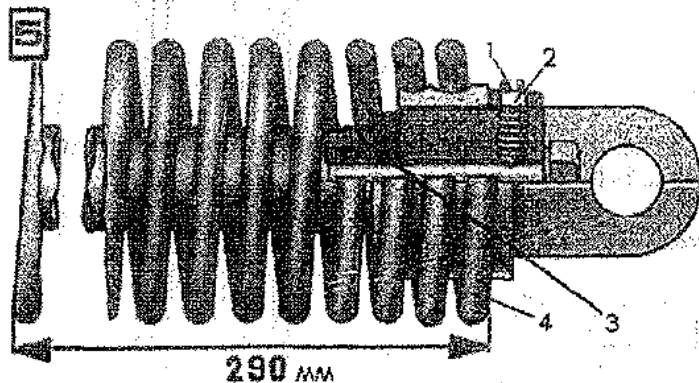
Схема регулировки длины пружины: 1 - винт стопорный; 2 - гайка; 3 - ось; 4 - натяжная пружина
